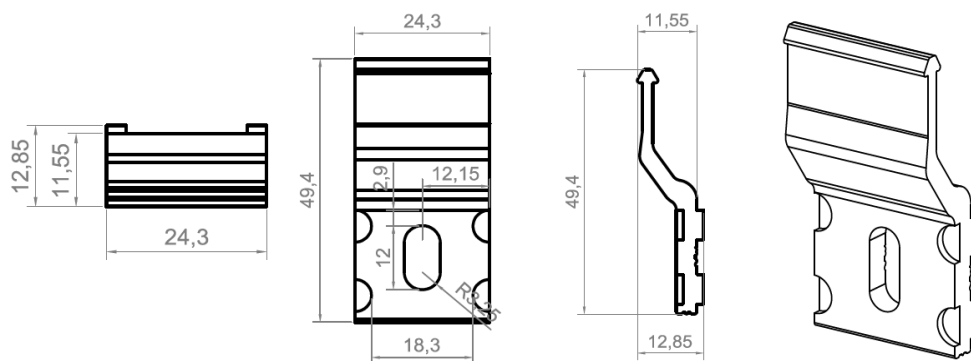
Soporte corto rigidizador horizontal CH (ref. 05.19.105)
